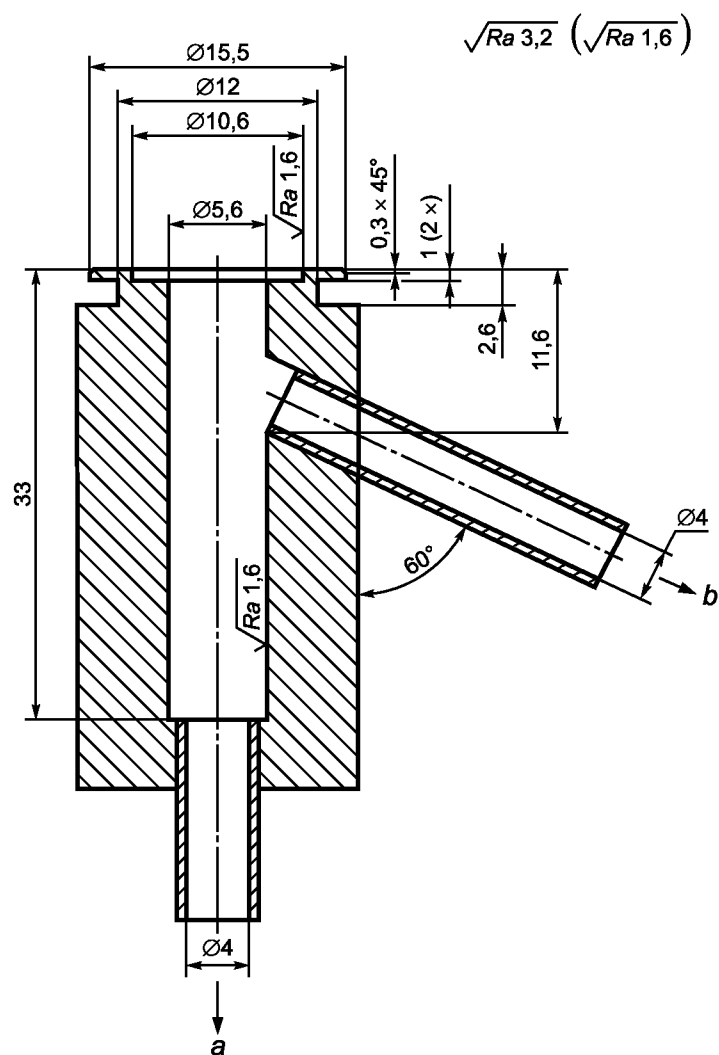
Общий вид контрольного блока. Расположение клапанов и портов
